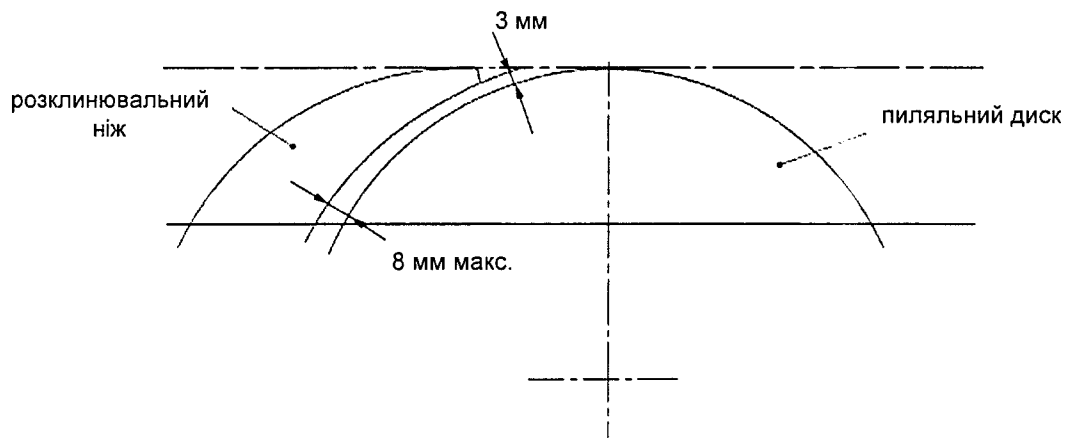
б) — Розміри для регулювання розклинювального ножа
